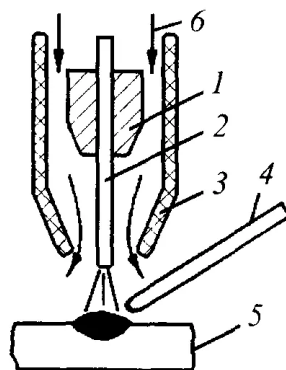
Схема сварки неплавящимся электродом в инертных газах:
